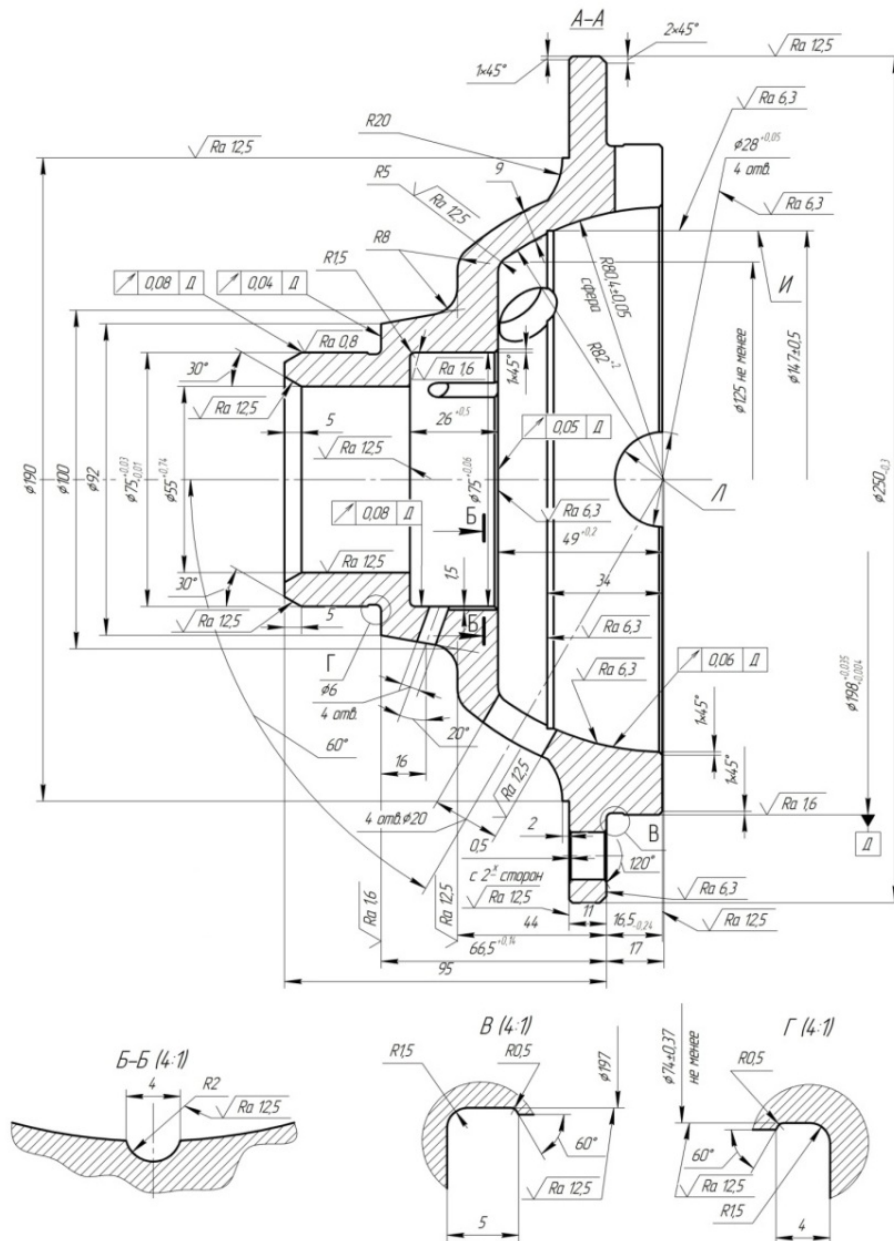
Чертеж детали 130-2403020-2 «Чашка дифференциала левая»
